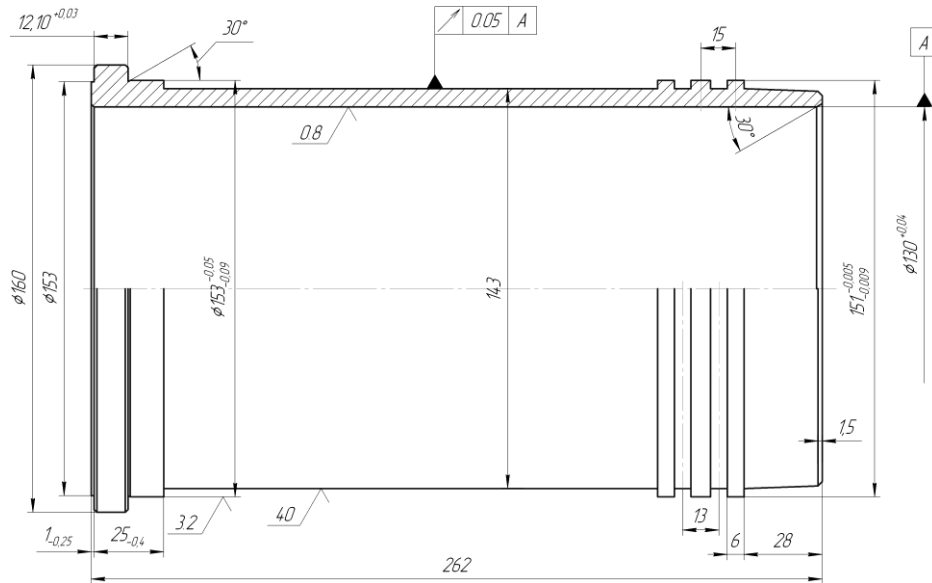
Загальний вигляд гільзи цилиндра двигуна
